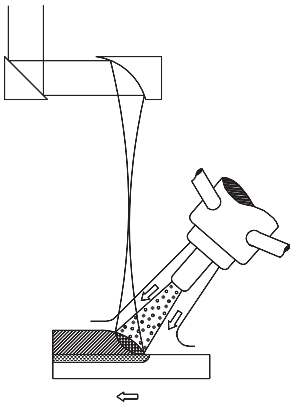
Prinzipskizze des Laserstrahl-Auftragschweißens mit seitlicher Pulverzufuhr
